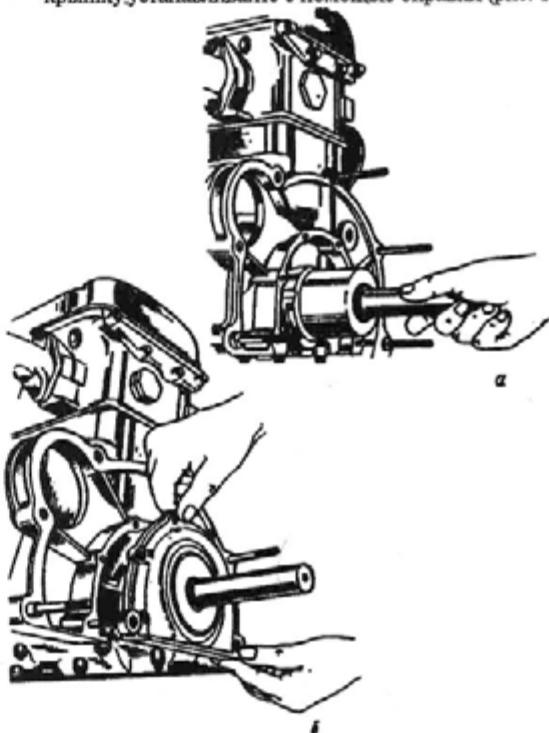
Установка крышки заднего сальника с помощью оправки:
